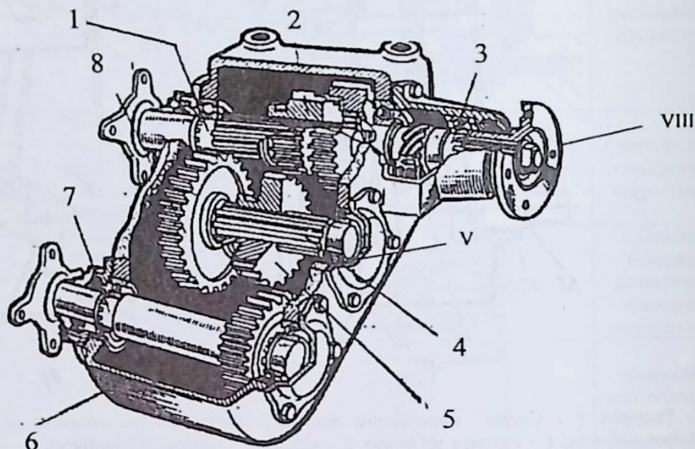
Роздавальна коробка автомобіля ГАЗ-66: 1 - ведучий вал; 2 - шестерня ввімкнення прямої або понижуючої передачі; 3 - введений вал; 4 - проміжний вал; 5 - шестерня ввімкнення переднього моста; 6 - картер; 7 - вал приводу переднього моста; 8 - шестерня понижуючої передачі; I - основні отвори, VIII - фланцеві отвори.
